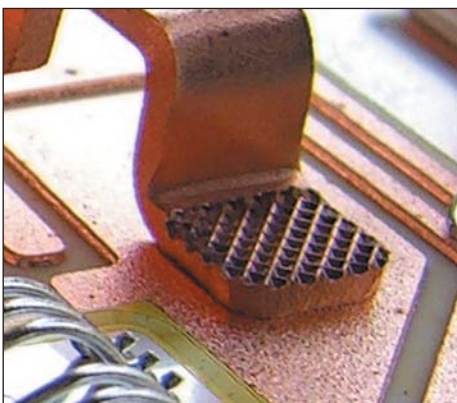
Медный вывод, приваренный к DBC ультразвуковой сваркой
